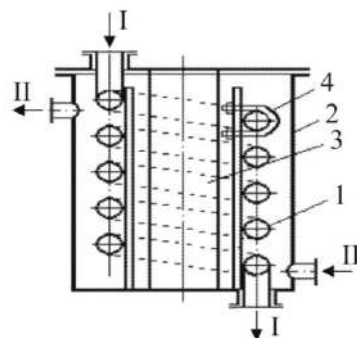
Змеевиковый теплообменник: 1 – спиральный змеевик; 2 – корпус аппарата; 3 – внутренний стакан; 4 – конструкция для крепления змеевика.
